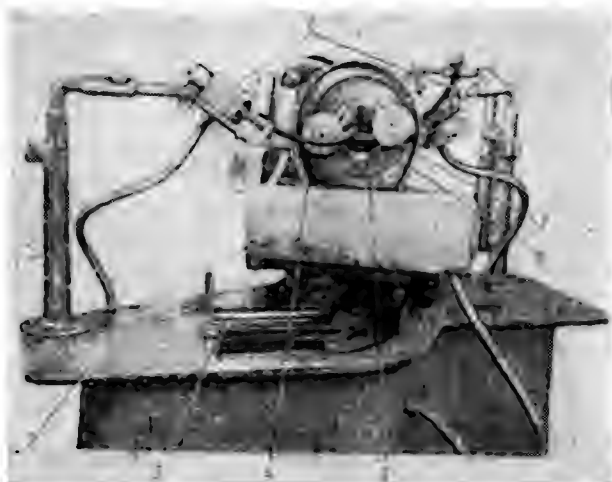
Полуавтоматический станок для наложения корпусной изоляции на катушки тяговых двигателей ДК-106:
